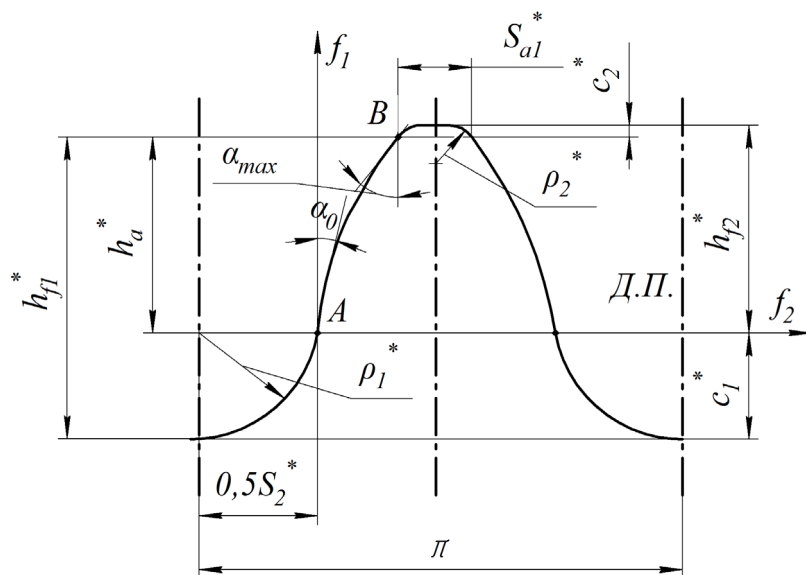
Схема профиля исходного контура внеполусной зубчатой передачи (ДП – делительная прямая)
